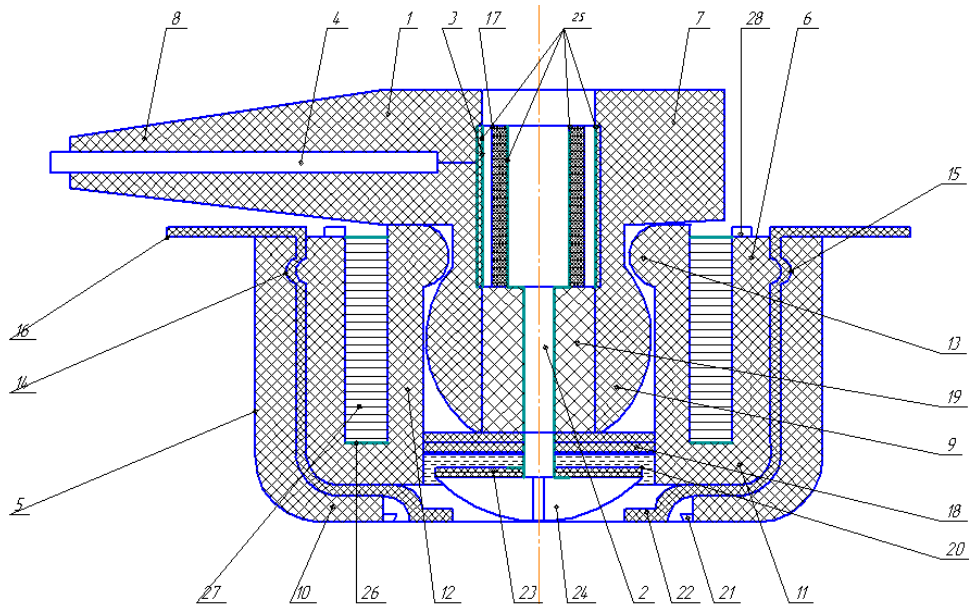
Універсальний первинний перетворювач, де 1 - корпус перетворювача; 2 - порожнина для заповнення гелем; 3 - струмознімач; 4 – відвідний дріт (провідники); 5 - підстава настановного гнізда; 6 - вкладиш установовочного гнізда; 7 - фланець корпусу перетворювача; 8 - гофрований хвостовик; 9 - кулясте стовщення на торці корпусу перетворювача; 10 – полка відбортовки основи установовочного гнізда; 11 – полка відбортовки вкладиша установовочного гнізда; 12- цангова засувка вкладиша установовочного гнізда; 13 - буртик на торці цангової засувки; 14 - поясок на зовнішній поверхні вкладиша установовочного гнізда; 15 - канавка на внутрішній поверхні основи установовочного гнізда; 16 - електропровідна тканина тримача електродів; 17 - втулка; 18 - прокладка; 19 - демпфер; 20 - погоджуючий шар; 21 - тримач п'єзоперетворювача; 22 - захисний ковпак; 23 - п'єзoeлемент; 24 - акустична лінза; 25 – контакти; 26 – каркас котушки індуктивності; 27 – багатовиткова котушка індуктивності; 28 – клеми котушки.
